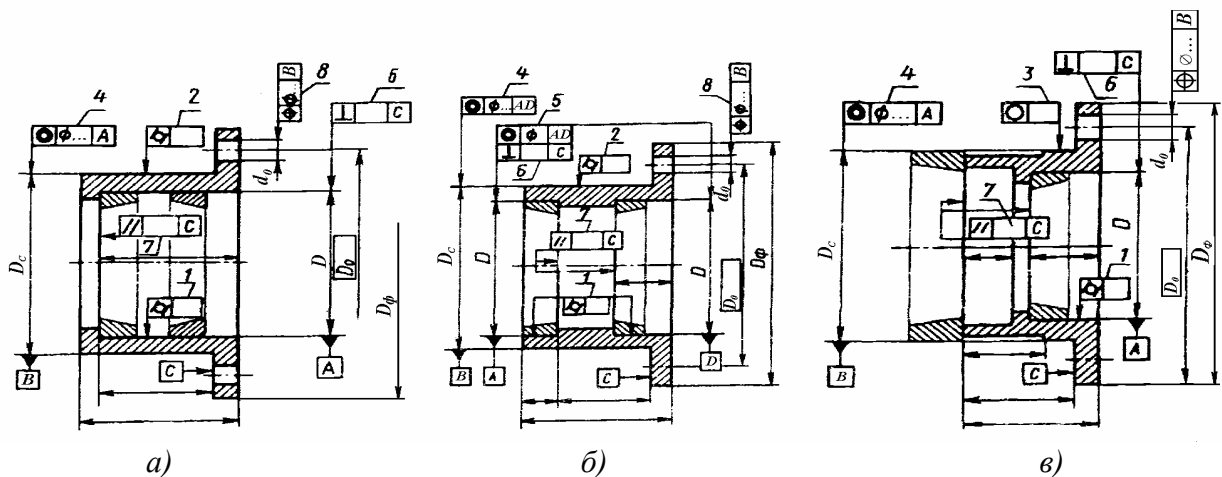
Обозначение на чертежах стаканов размеров, баз, допусков формы и расположения
